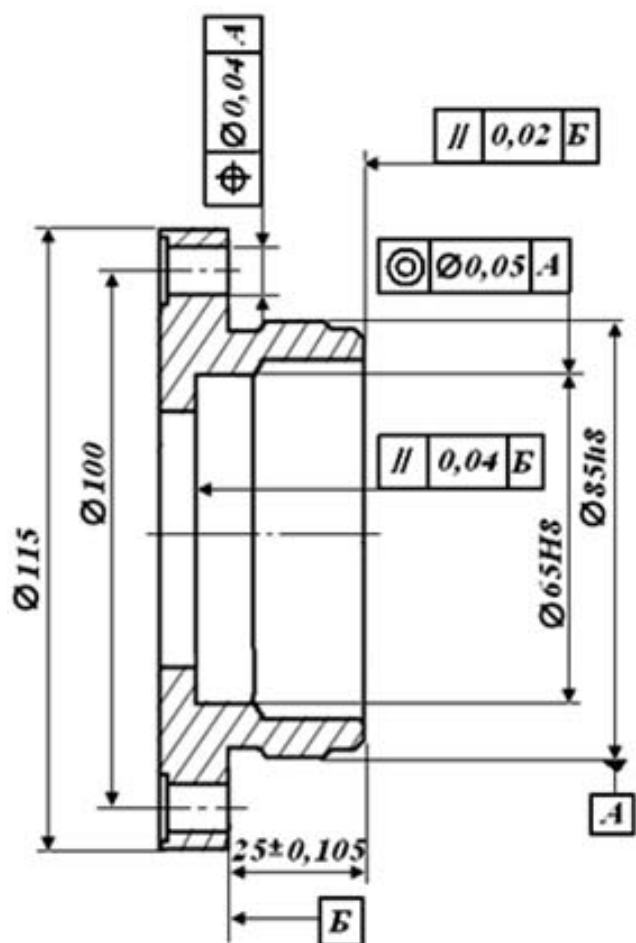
Ескіз кришки з зазначенням баз, допусків форми і розташування поверхонь
